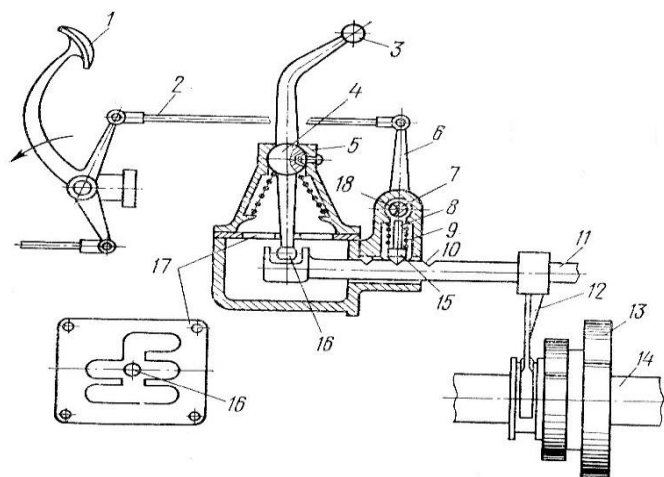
Механизм переключения передач: 1 – педаль; 2 – тяга; 3 – рычаг переключения передач; 4 – сферическая опора рычага; 5 – корпус опоры; 6 – рычаг; 7 – валик; 8 – стержень фиксатора; 9 – пружина фиксатора; 10 – углубление ползуна; 11 – ползун; 12 – вилка; 13 – каретка; 14 – вал; 15 – фиксатор; 16 – нижняя часть рычага управления; 17 – пластина
